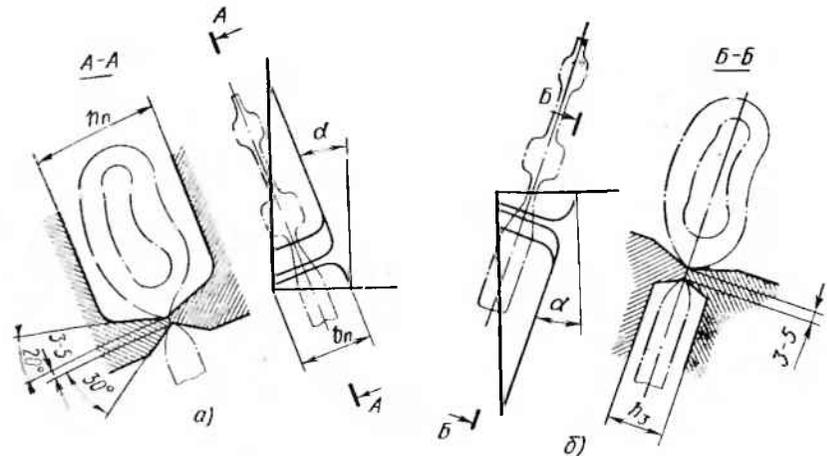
Ножи для отрубки поковки от прутка на молоте:
